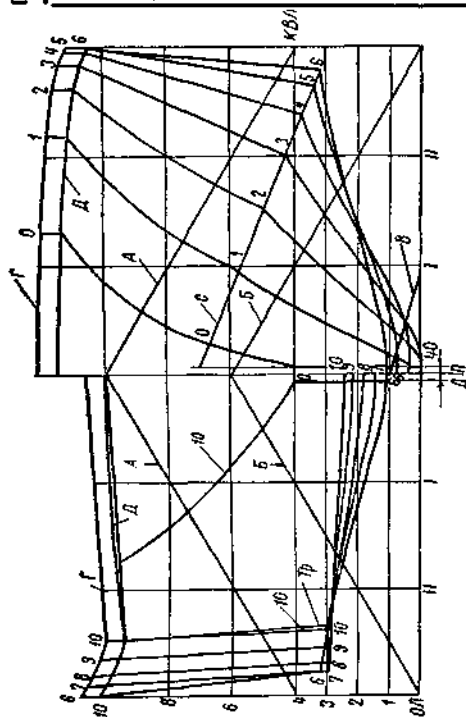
Теоретический чертеж: а — проекция «Бок» и «Полуширота»; б — проекция «Корпус».
